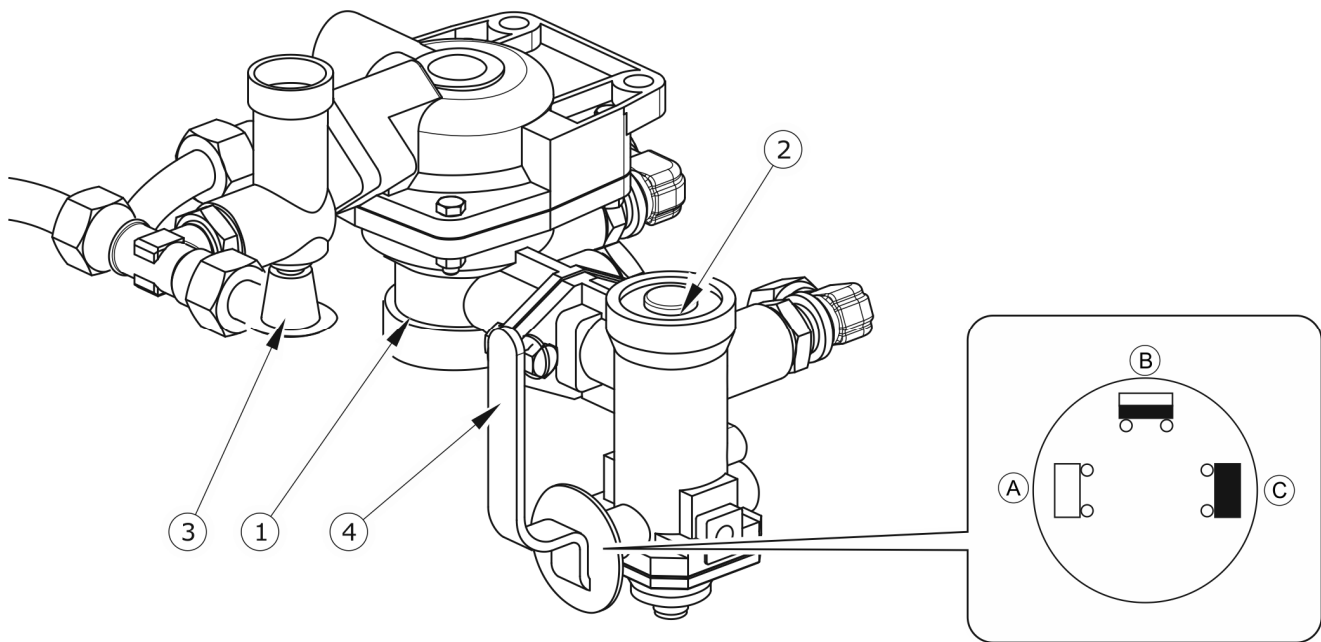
Válvula direccional y regulador de la fuerza de frenado
